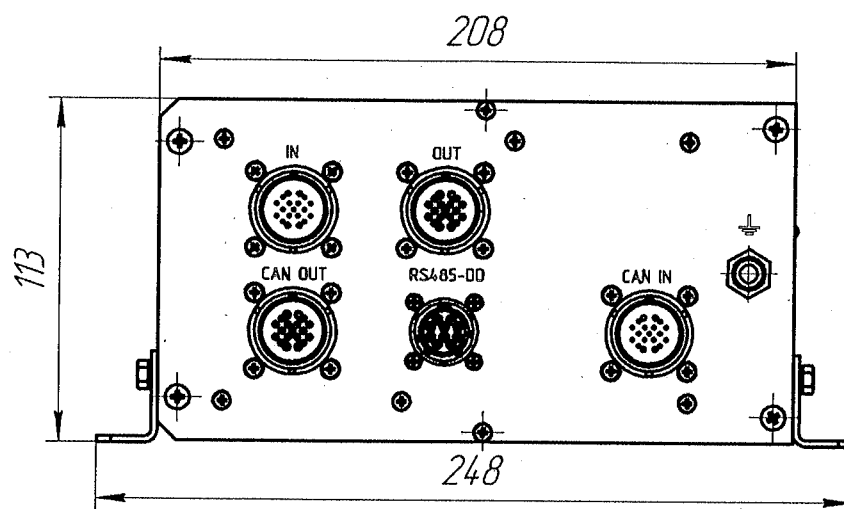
Внешний вид блока ВВД-01 36311-40-00-01
